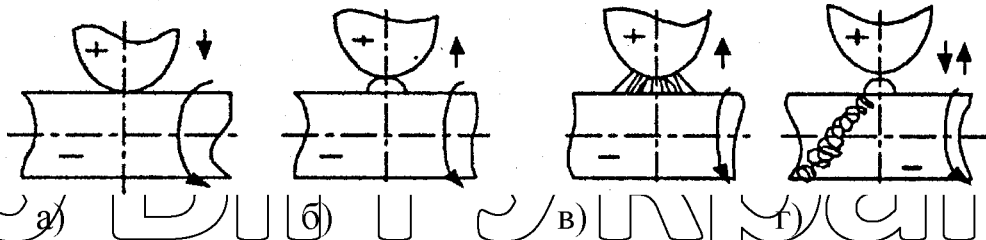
Схеми для формування валика за вібродугового наплавлення.
